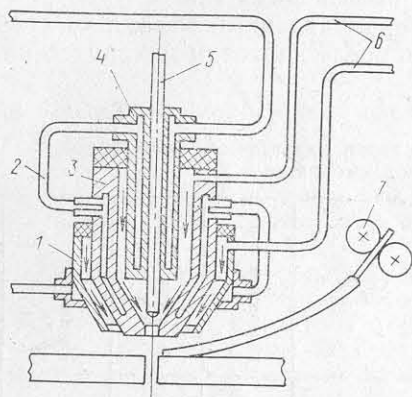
Схема сварки алюминиевых сплавов сжатой дугой переменного тока и устройство плазмотрона.
